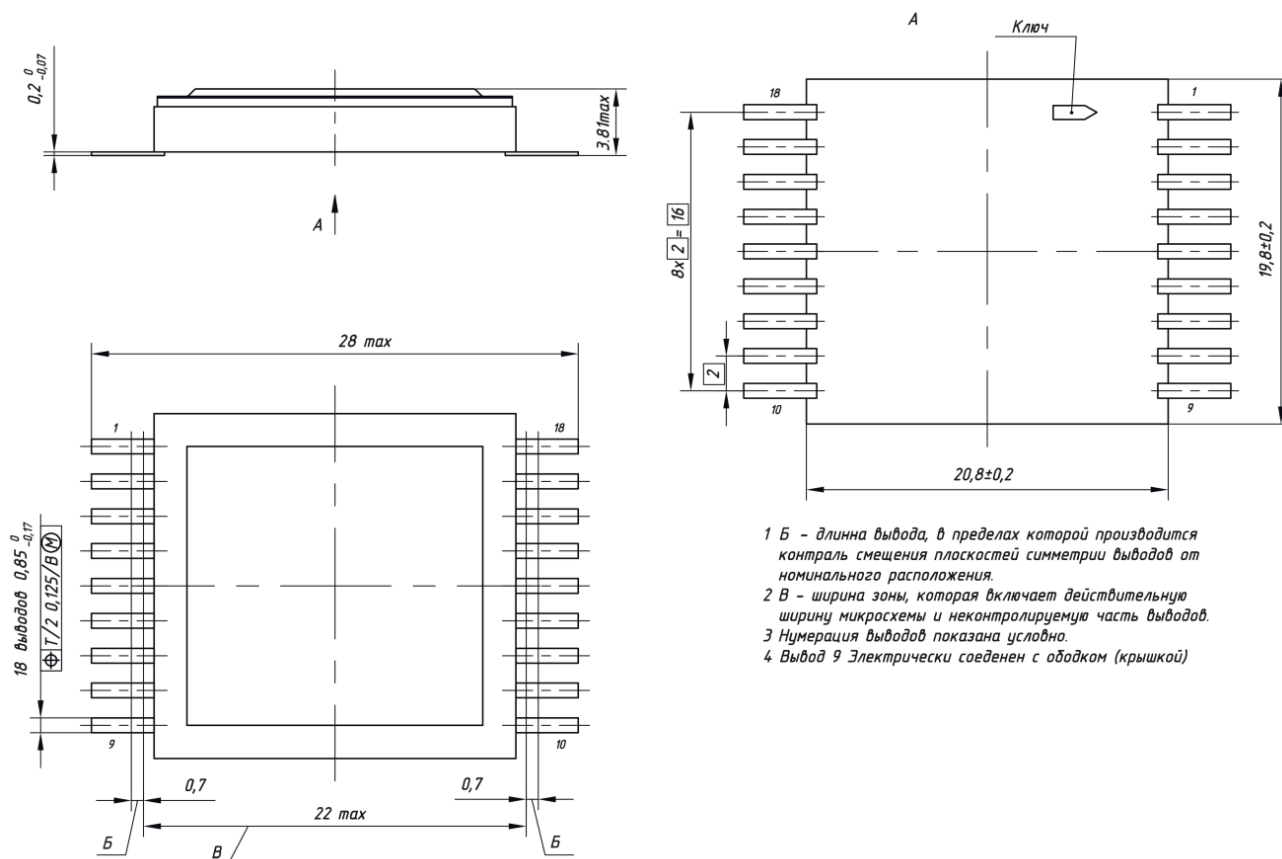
Габаритный чертеж корпуса "Марабу"
